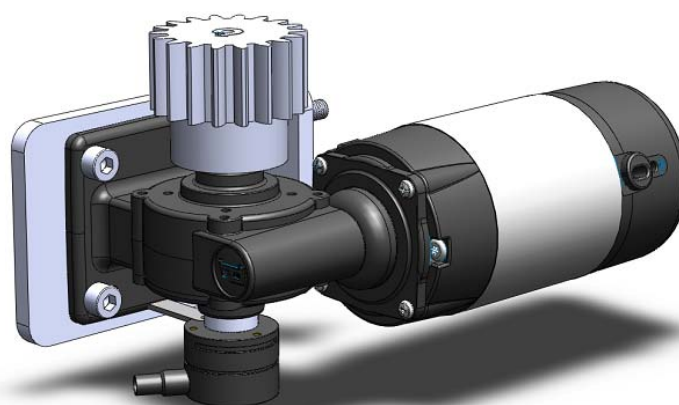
Motor, engrenagem e placa de suporte do ISASC.
